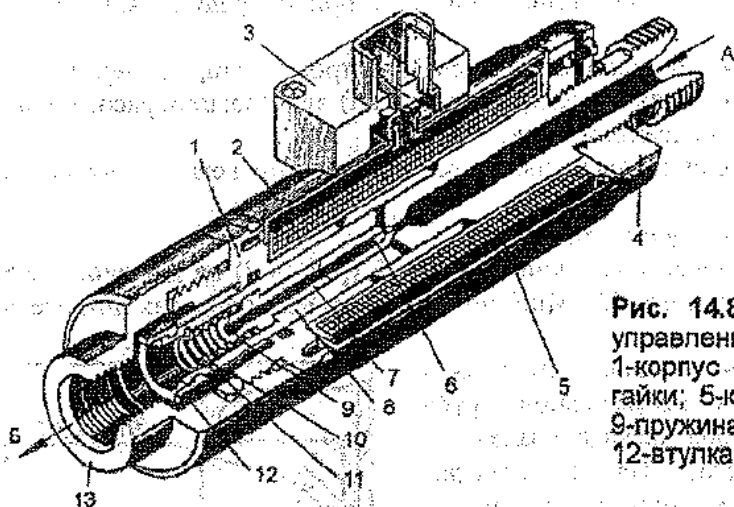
Гидроклапан с электромагнитным управлением КЭ-1,6-2,5-16-01 или 109.00.000В: 1-корпус катушки; 2-гильза; 3-клемма; 4, 13-гайки; 5-катушка; 6-игла; 7-толкатель; 8-якорь; 9-пружина; 10-шайба; 11-кольцо стопорное; 12-втулка; А, Б-отверстия
